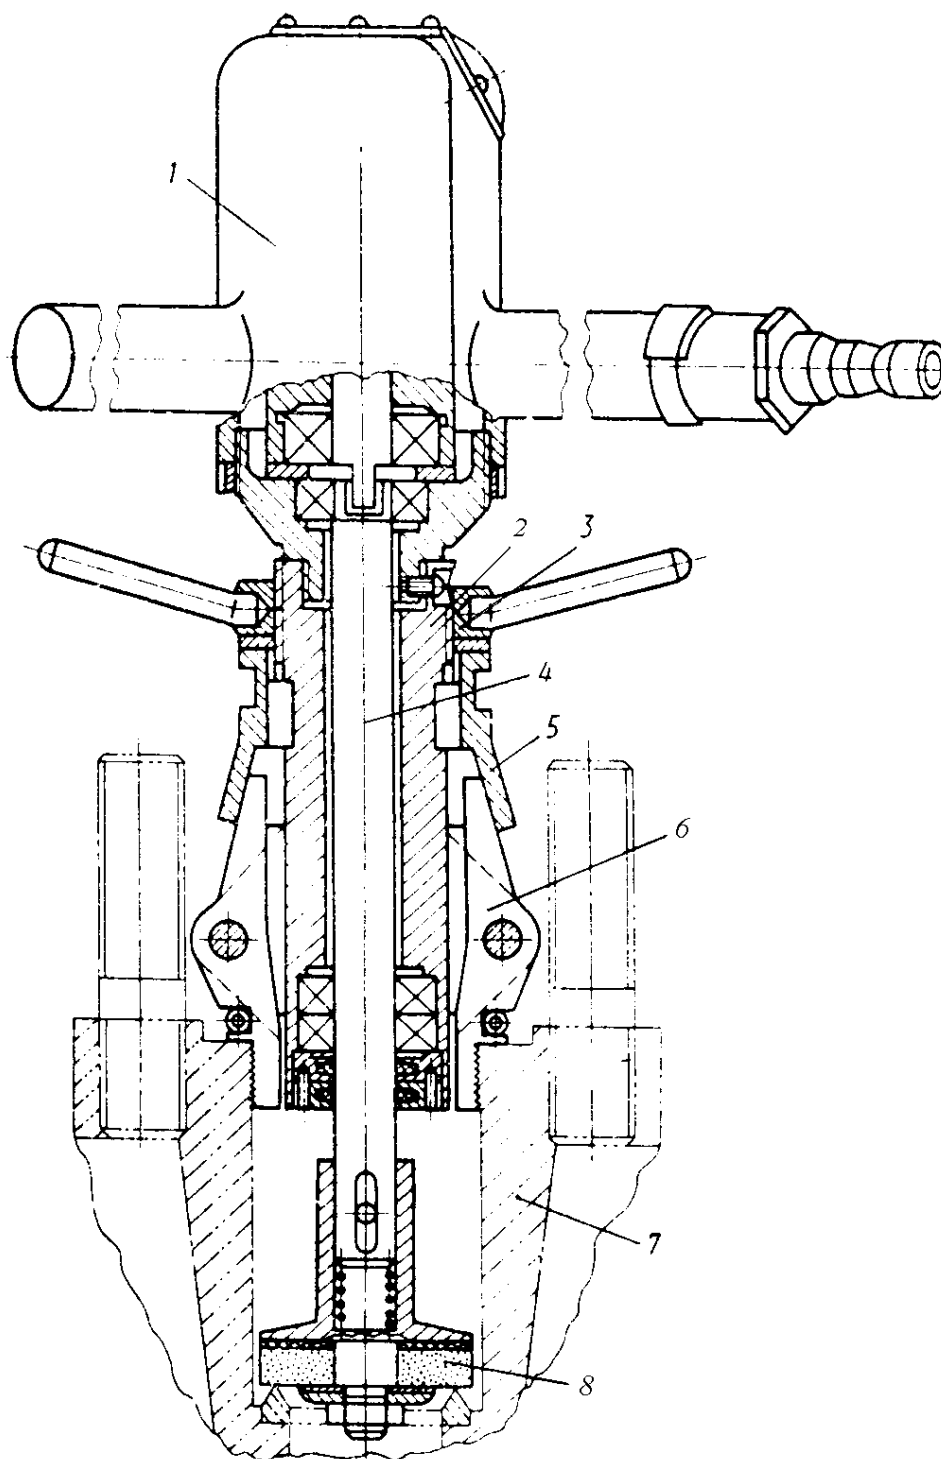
Приспособление для шлифовки седел вентиля $D_y 50$ мм.
